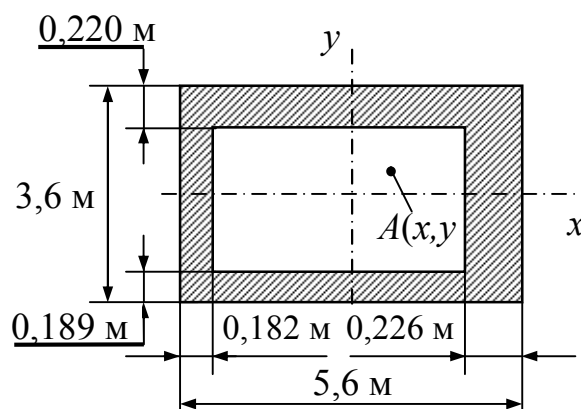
Поперечное сечение обрабатываемой корпусной детали
